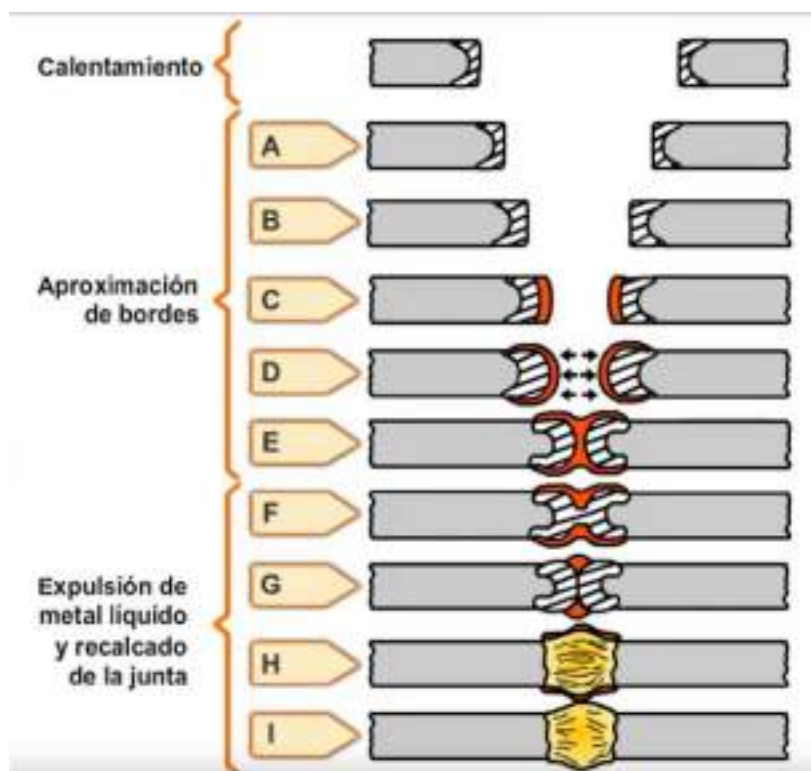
Representación de las “aletas” o bordes al soldarse.
